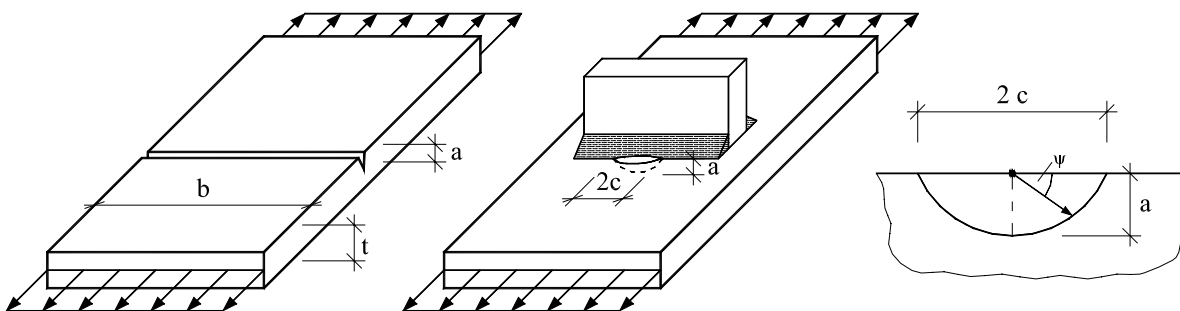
a) durchgehender Riß b) halb-elliptischer Oberflächenriß am Schweißnahtfußpunkt
